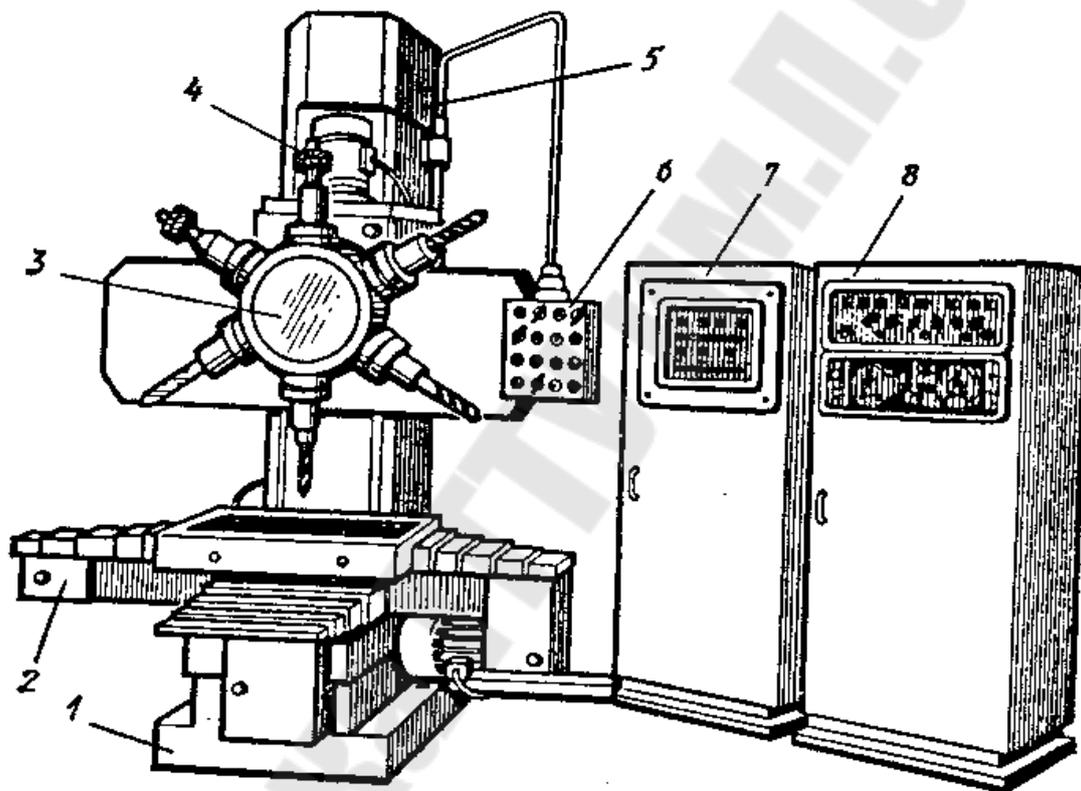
Общий вид вертикально-сверлильного станка с ЧПУ
